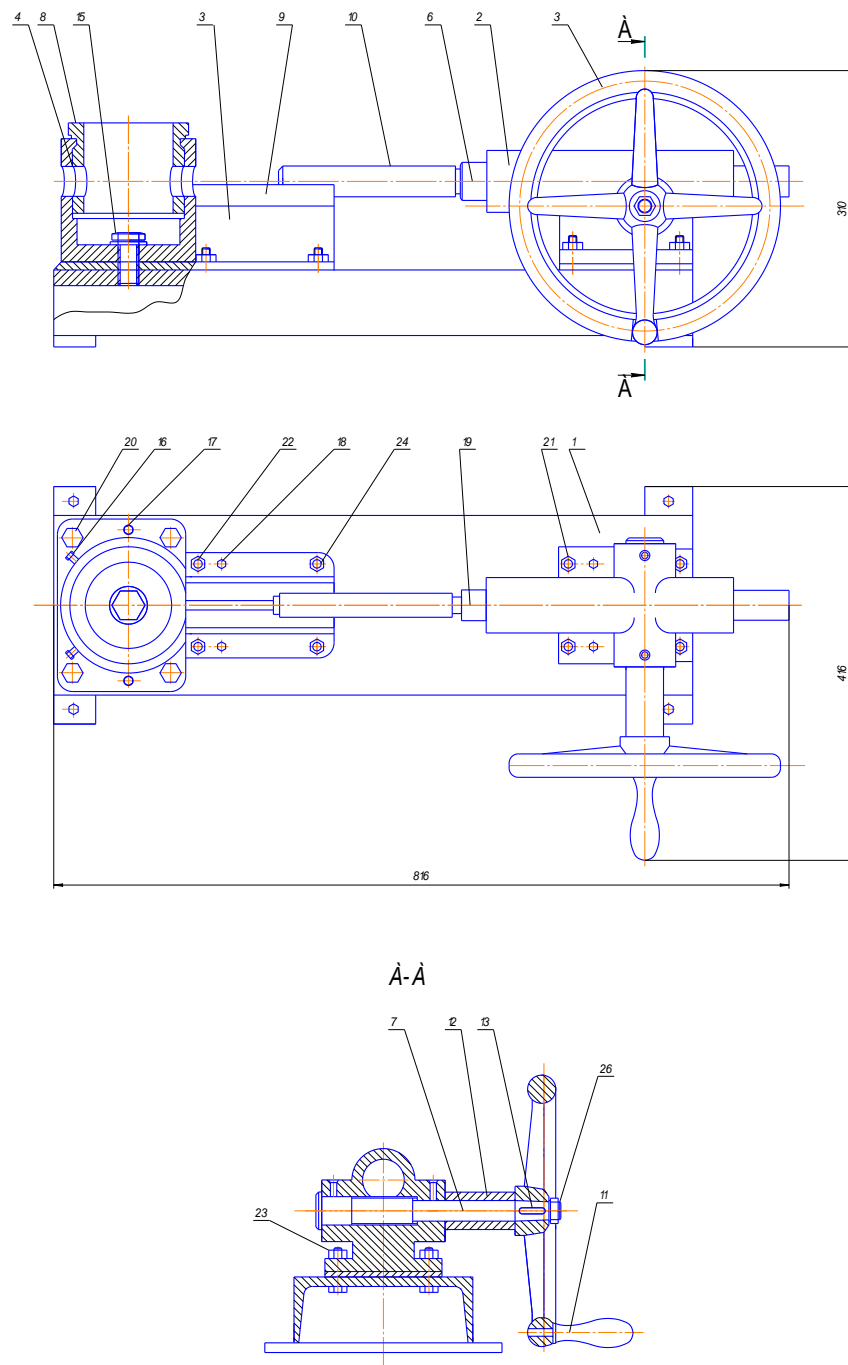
Креслюнок розробленого пристосування для збирання шатуна з поршнем: 1 – станина; 2 – основа рейки; 3 – опора призми; 4 – основа стакана; 5 – маховик; 6 – рейка; 7 – вал; 8 – змінний стакан; 9 – змінна призма; 10 – штовхач змінний; 11 – рукоятка; 12 – розпірна втулка; 13 – півкругла шпонка; 14 – болт; 15 – контргайка; 16 – гвинт; 17, 18 – штифт; 19 – стопорний гвинт; 20, 21, 22 – болт; 23, 24, 25 – гайка; 26 – шайба
